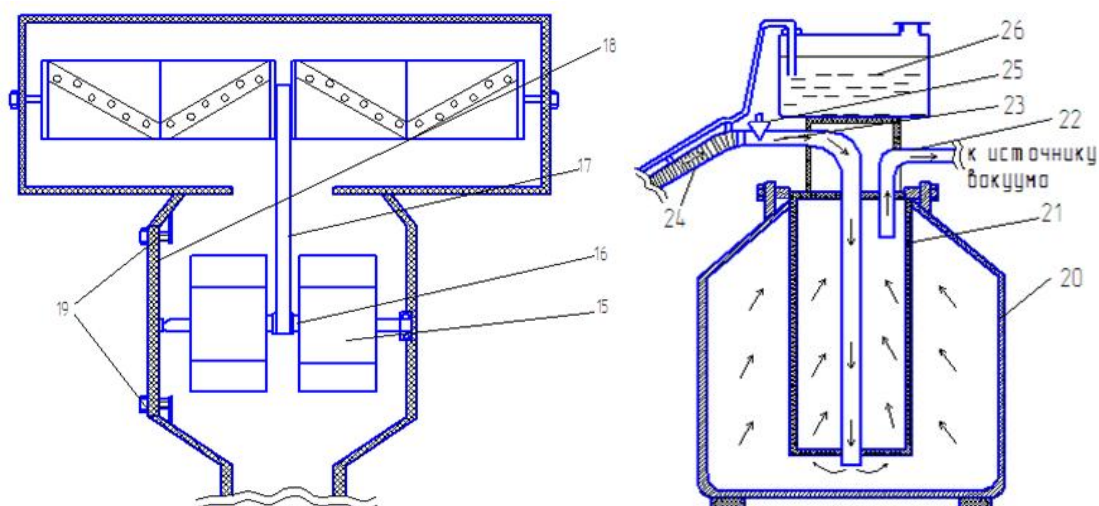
Устройство для очистки кожного покрова. Вид сверху. Сборник для пыли.
